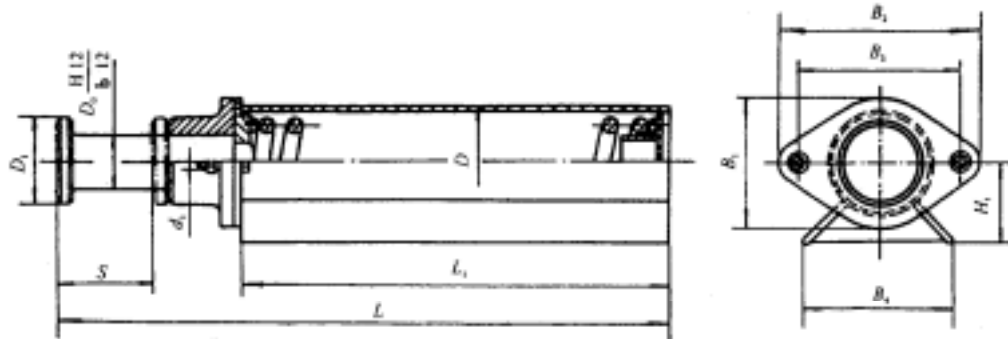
HT2 型底座焊接式弹簧缓冲器
